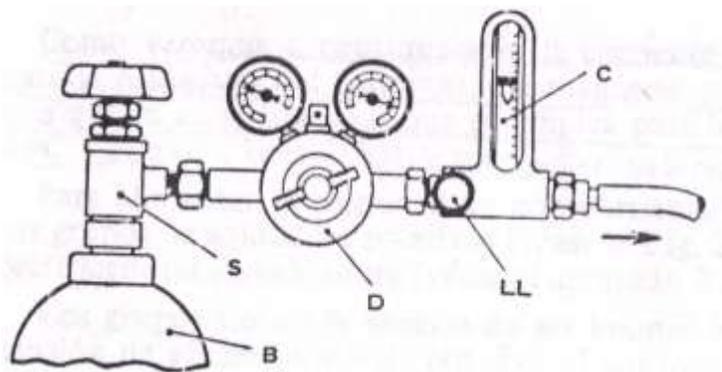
Equipos utilizados para la soldadura TIG
